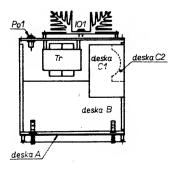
Laboratorní zdroj – pohled ze spodní strany
